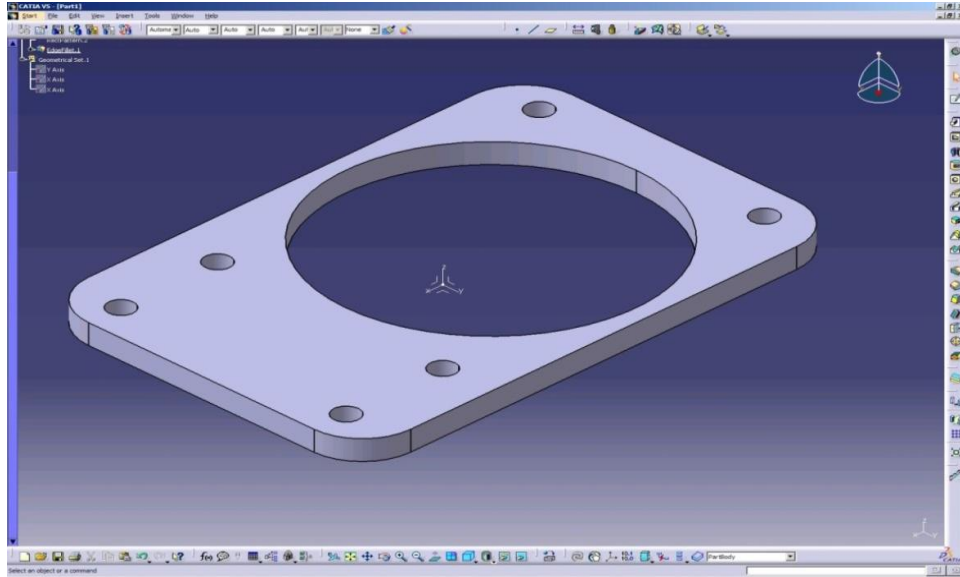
Imagen CAD diseño del soporte para el ensamble.
